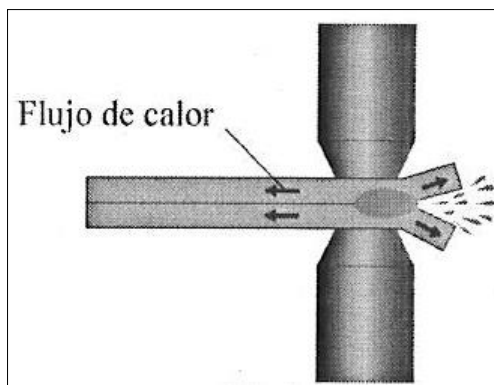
Efecto de ubicar el punto de soldadura cerca del extremo de la hoja de acero.
